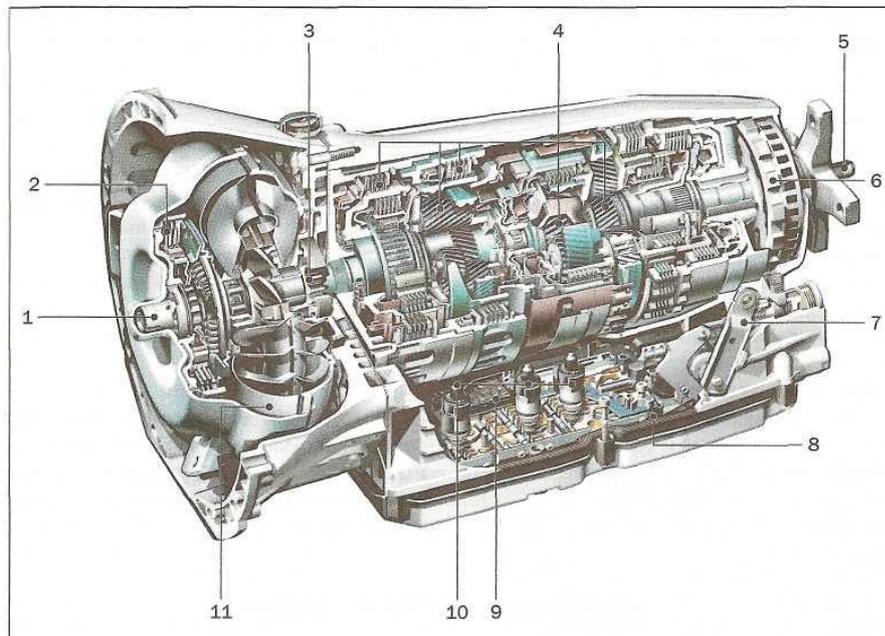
Пристрій коробки передач 7G-Tronic:
